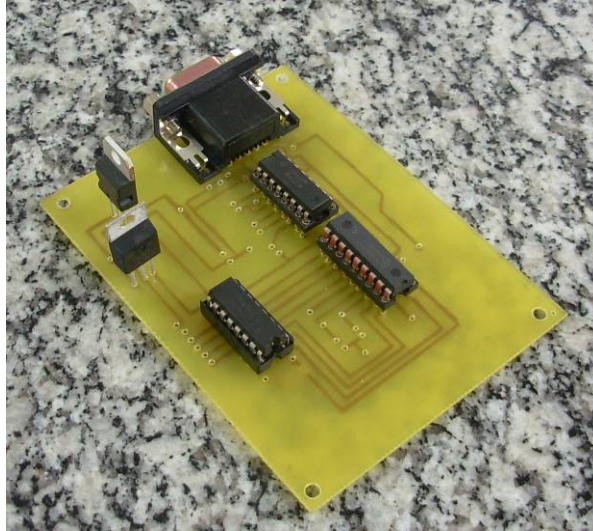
Placa de circuito com alguns componentes soldados
